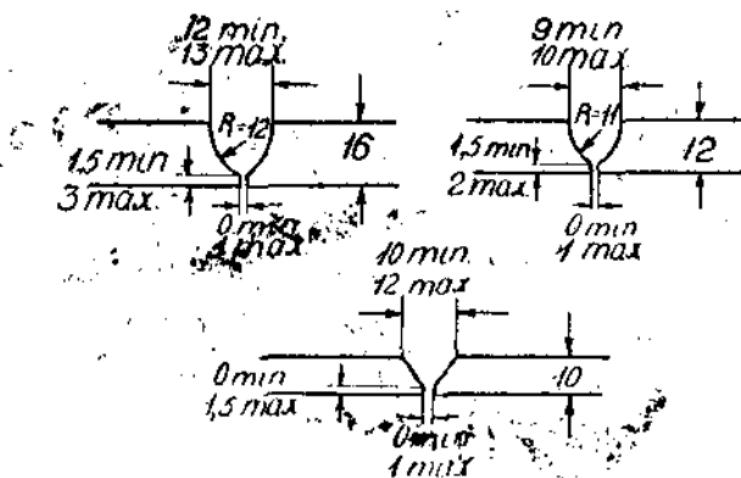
Подготовка кромок для стыковой автоматической сварки.
